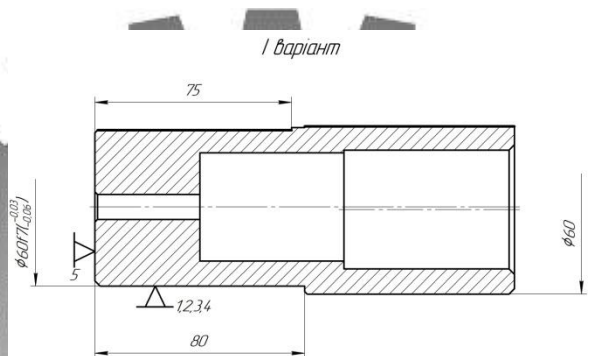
Схема базування заготовки на фрезерній операції I варіант.
